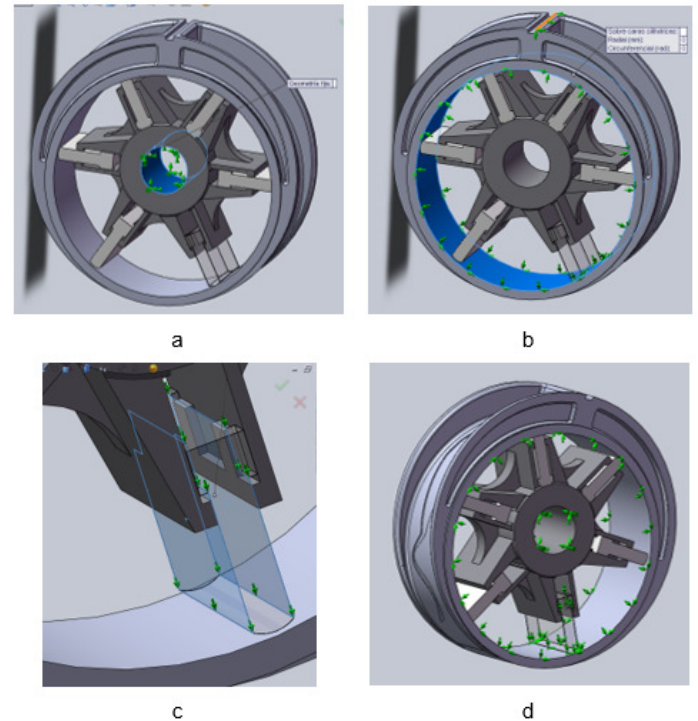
Sujeción en el conjunto Anillo Rotor Paleta a) Sujeción de geometría fija en el rotor, b) sujeción de geometría fija en el anillo, c) sujeción de restricción deslizante sobre caras planas en la paleta, d) conjunto con restricciones de movimiento. Fuente: Autor del proyecto
